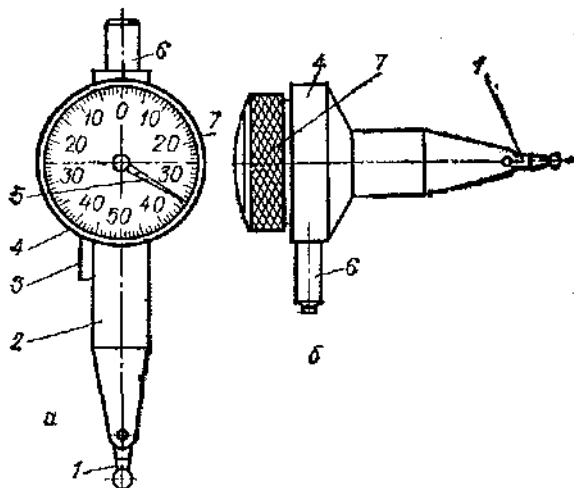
Рычажно-зубчатый индикатор бокового (ИРБ) и торцового (ИРТ) действия:
